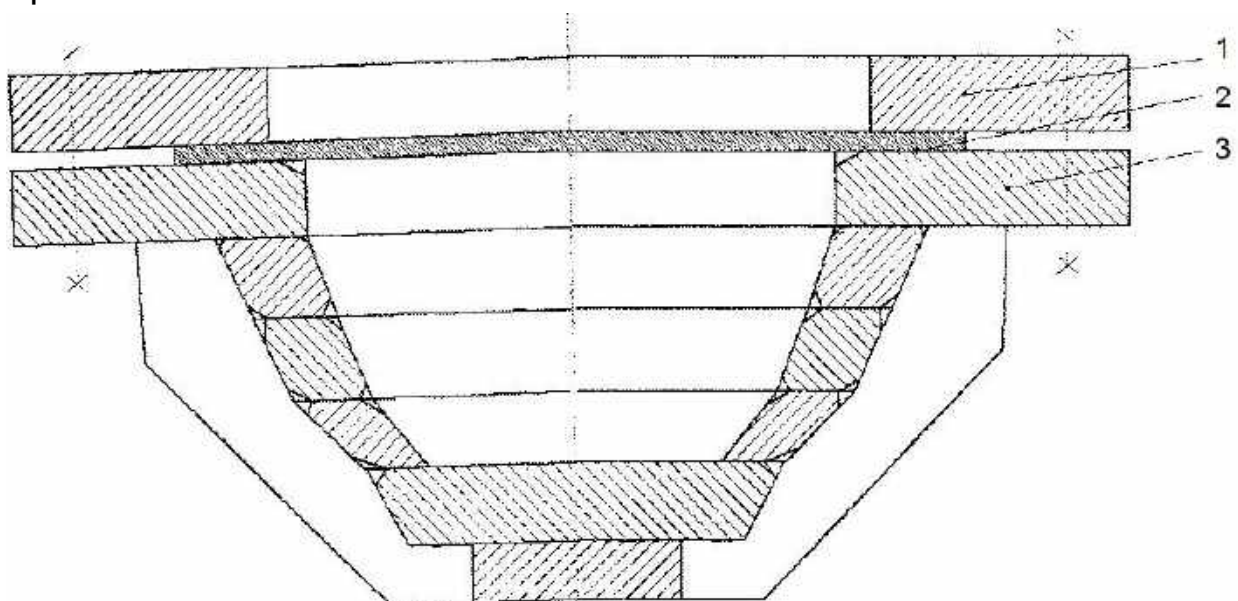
Штамп з матрицею, звареною зі сталевих кілець: 1 – корпус матриці; 2 – притискне кільце; 3 – заготовка
